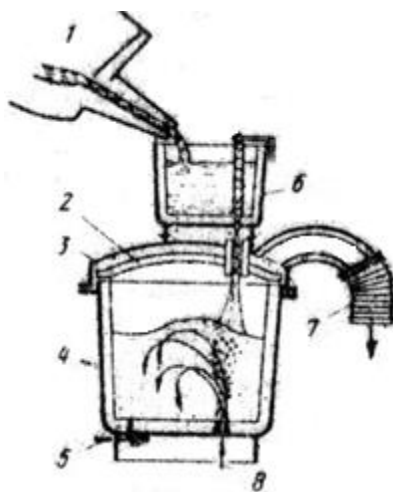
Схема дегазации стали струйным вакуумированием во время выпуска: 1 – сталеплавильный агрегат; 2 – защитный экран; 3 – крышка ковша; 4 – сталеразливочный ковш; 5 – шиберный затвор; 6 – промежуточный ковш со стопором; 7 – патрубок для отвода газов; 8 – подача инертного газа
